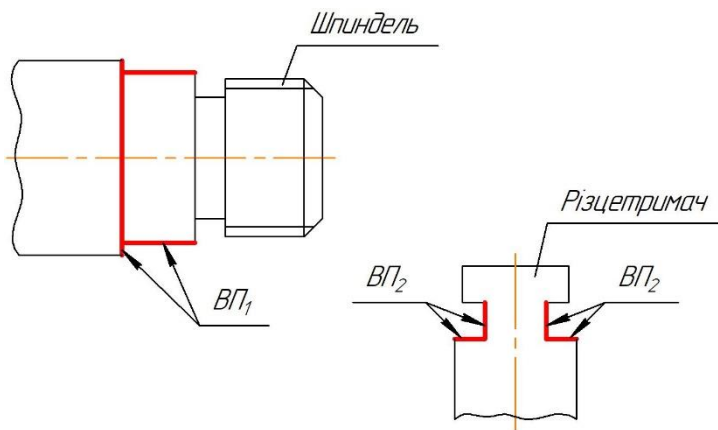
Виконавчі поверхні під час оброблення валика в патроні
